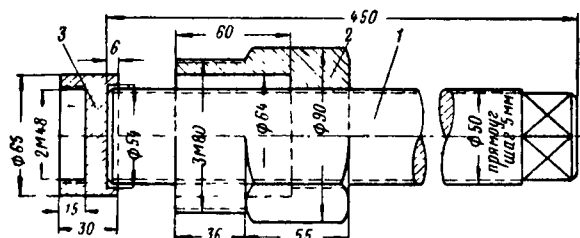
Приспособление для распрессовки якоря генератора управления ДК-405:
